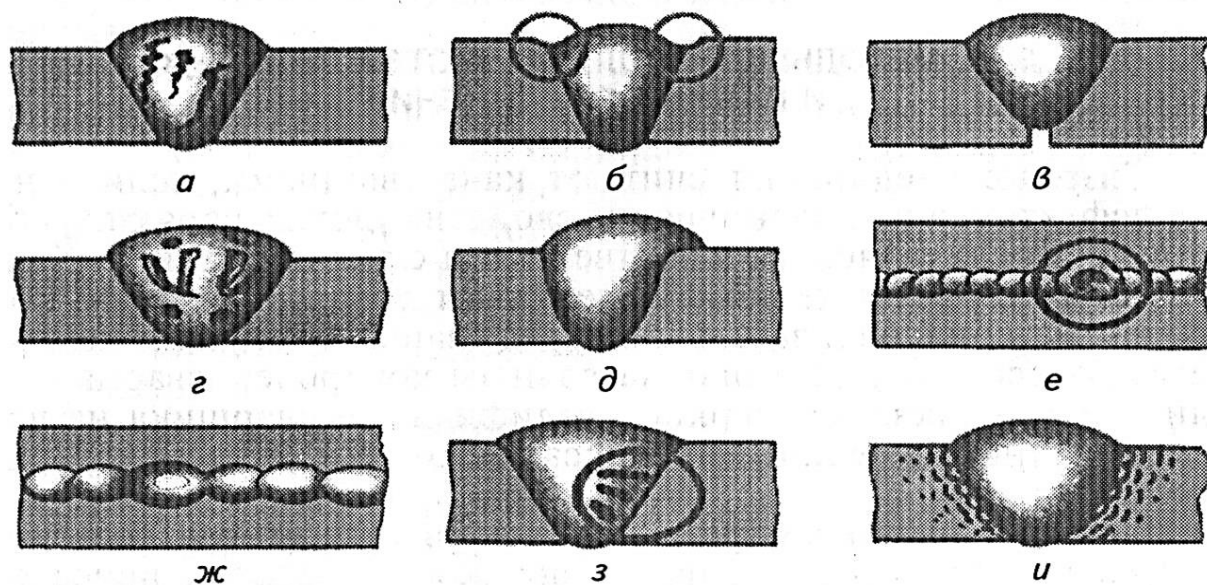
Дефекты сварных соединений: а – трещины; б – подрезы; в – непровары; г – поры и раковины; д – наплывы; е – кратеры; ж – прожоги; з – неметаллические включения; и – перегрев
